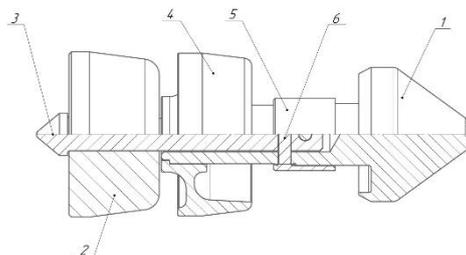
Предлагаемая конструкция спутника с оправкой: 1 – головка; 2 – оправка; 3 – шпилька; 4 – втулка; 5 – гайка; 6 – штифт
